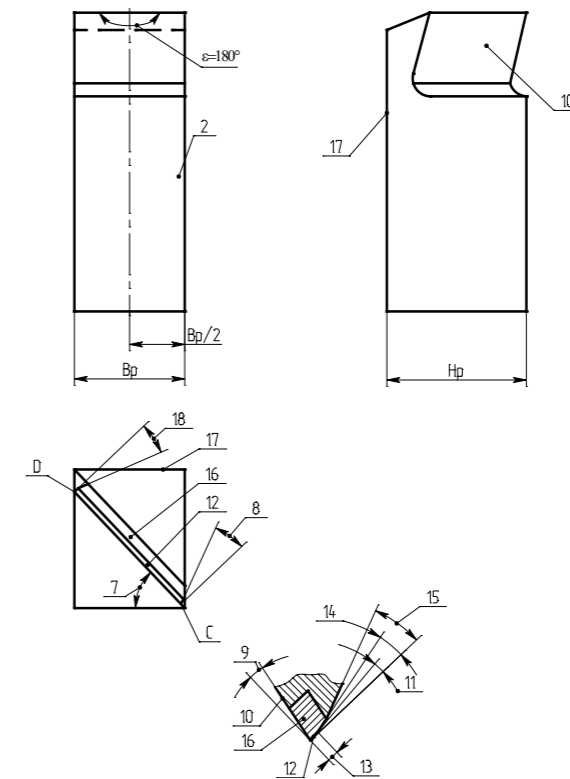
Конструкция безвершинного токарного проходного резца
